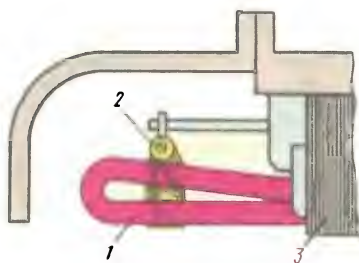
Лобовые части обмотки статора, крепление бандажными кольцами:
